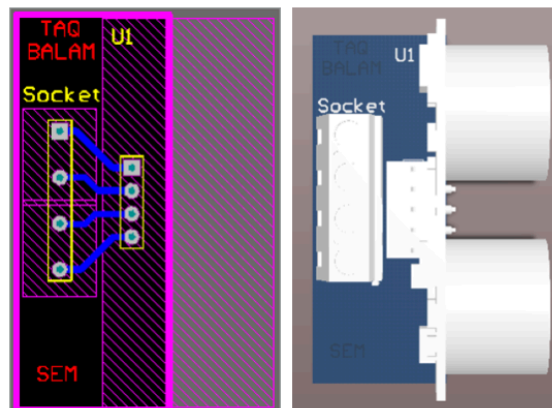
Diseño del circuito impreso del sensor infrarrojo
